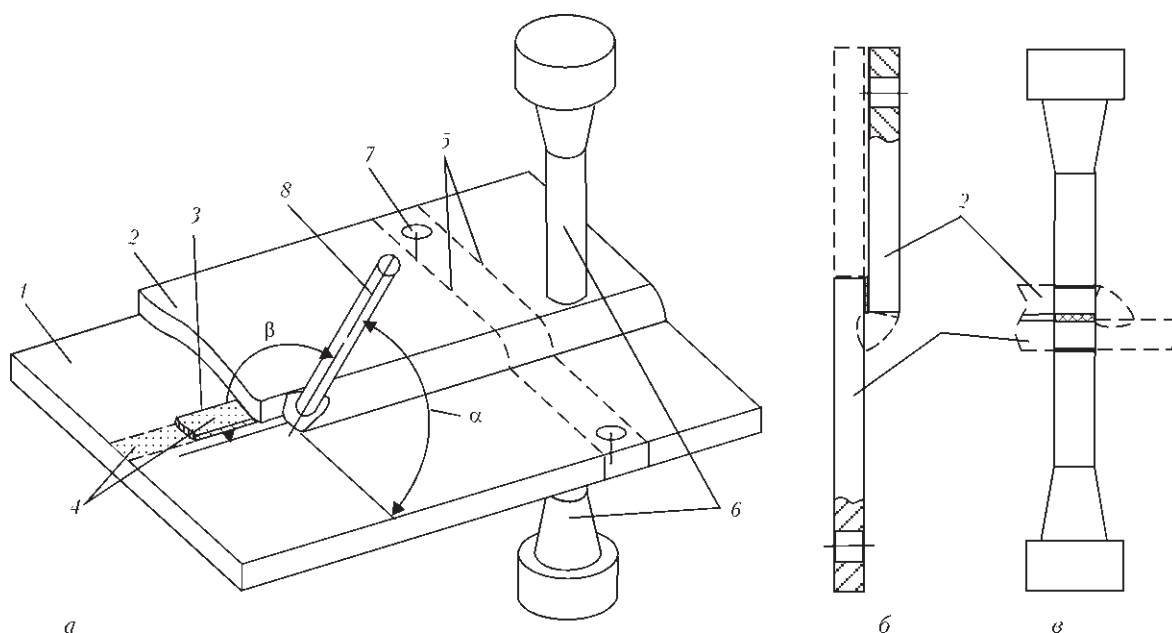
Схема подготовки образцов для испытания паяного участка на разрыв и срез: *а* — сварка с сопутствующей пайкой; *б* — образец тип V; *в* — образец тип II
